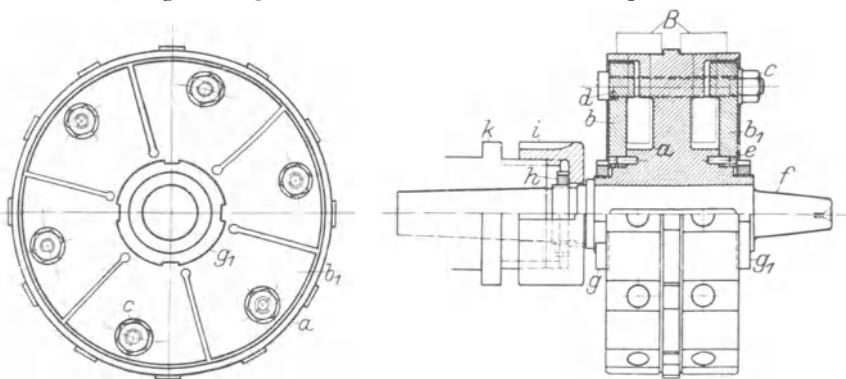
Schraubenkopf-Fräsvorrichtung.
